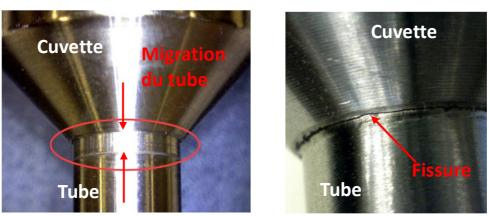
Inspection de la soudure : Exemples de dommages
